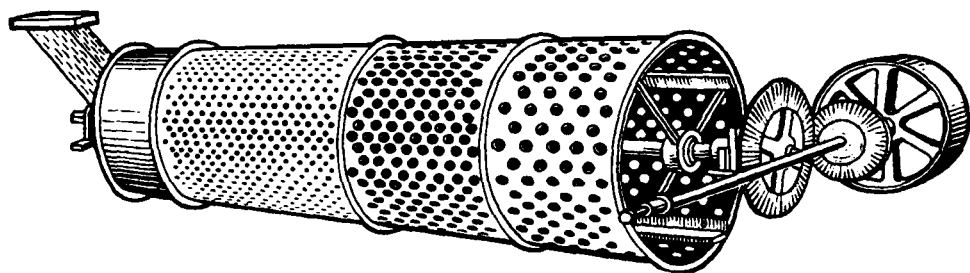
Конструкция барабанного грохота с последовательным расположением сит
